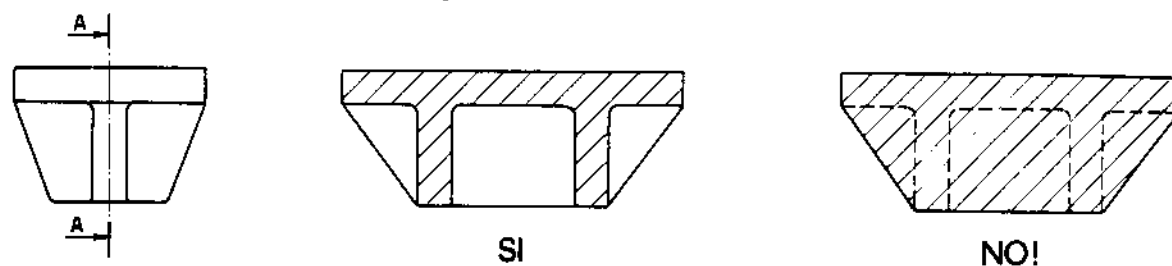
Le nervature non si sezionano quando il piano di sezione è longitudinale.
